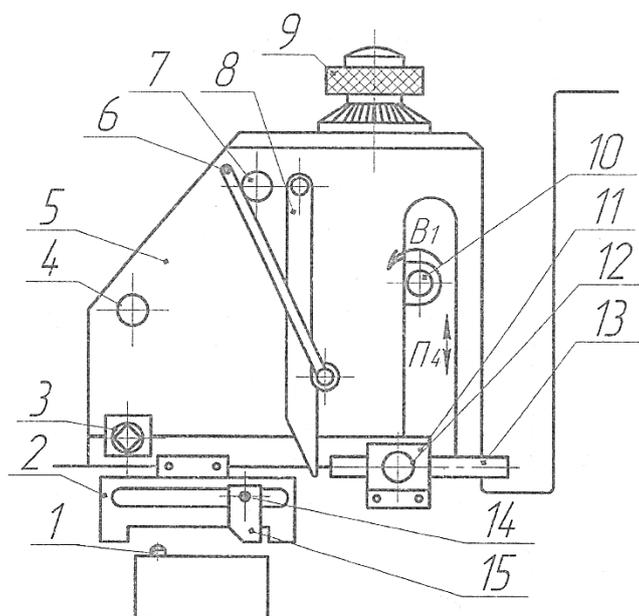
Шпиндель зубофрезерного станка 5А308П
